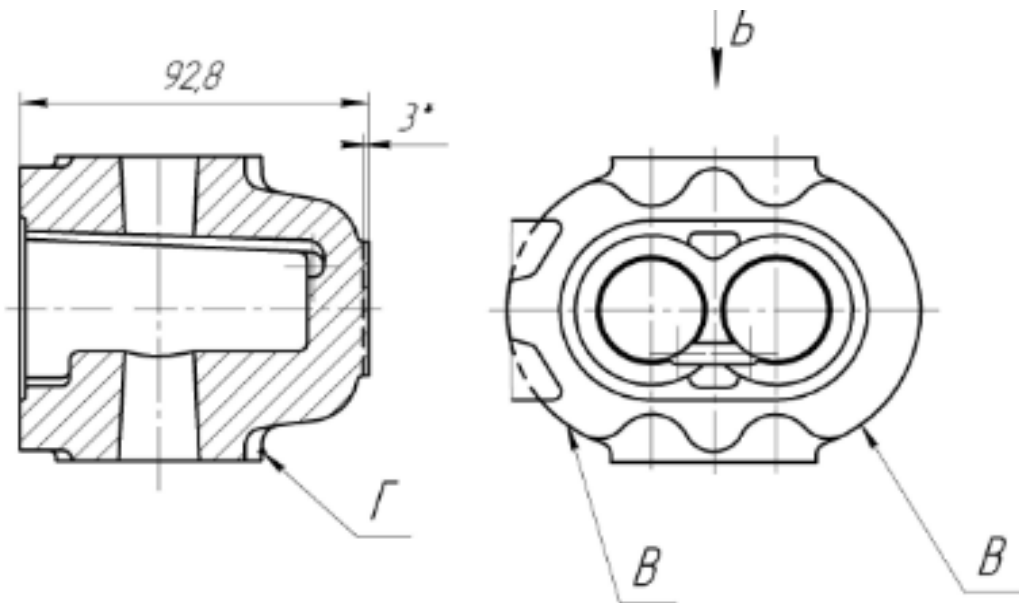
Виливок деталі в розрізі та вигляд зверху
